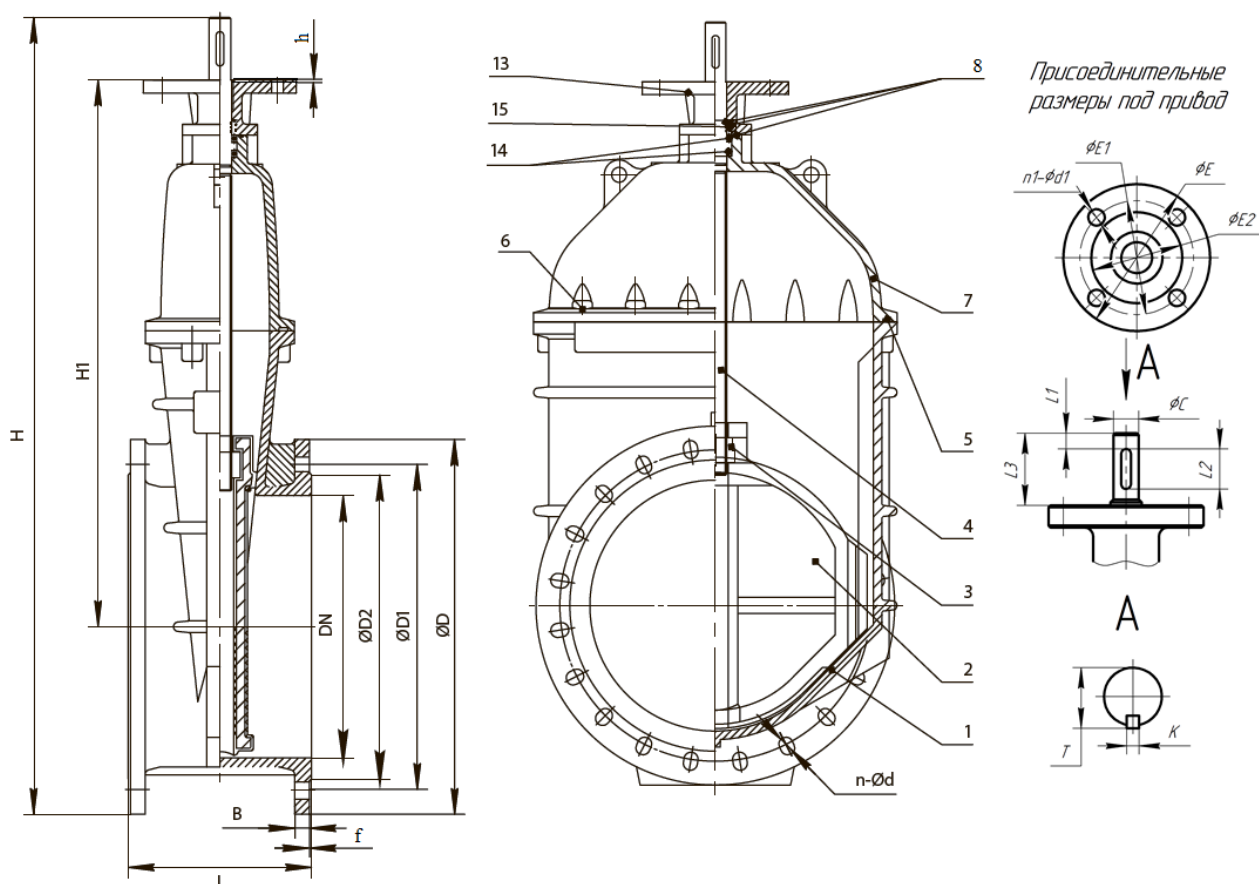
Задвижка 47GVA без исполнительного механизма DN700-1000
